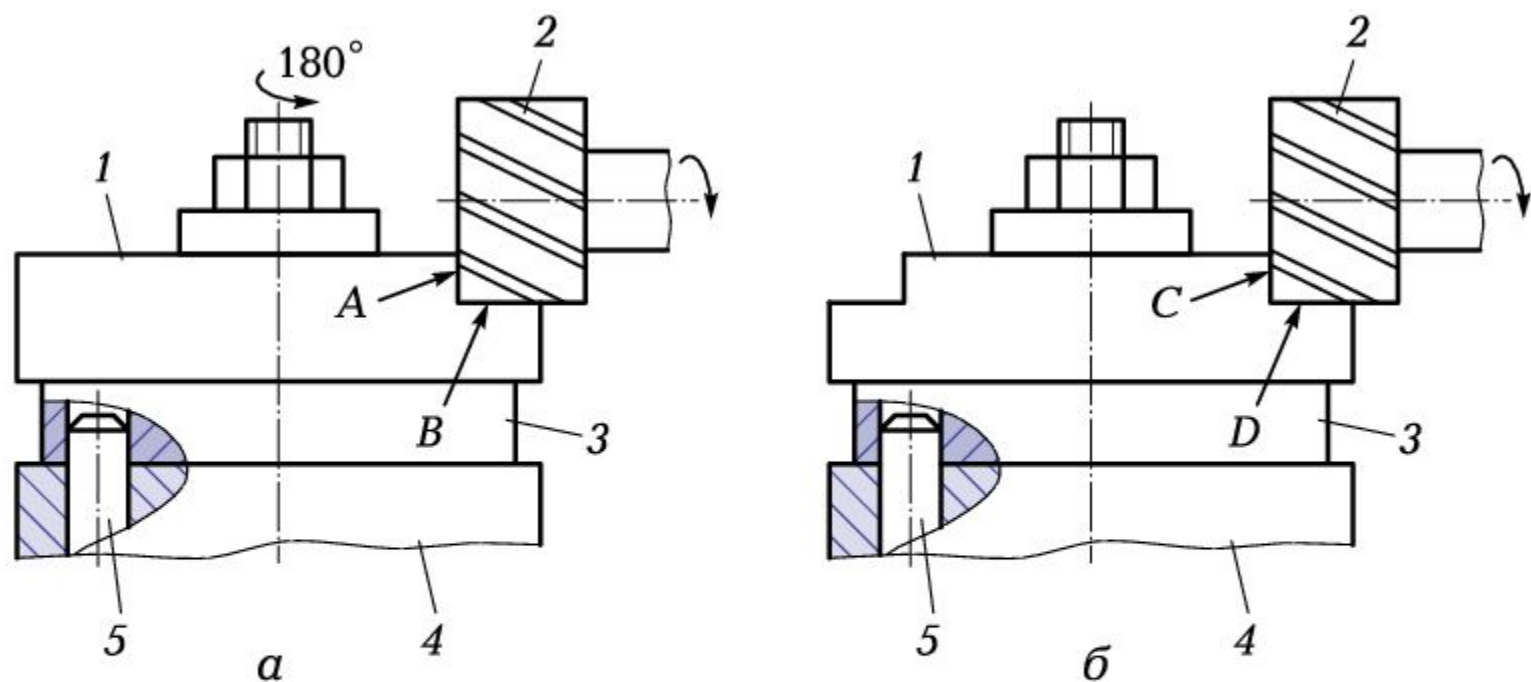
Схемы (а, б) обработки заготовки в двух позициях:
